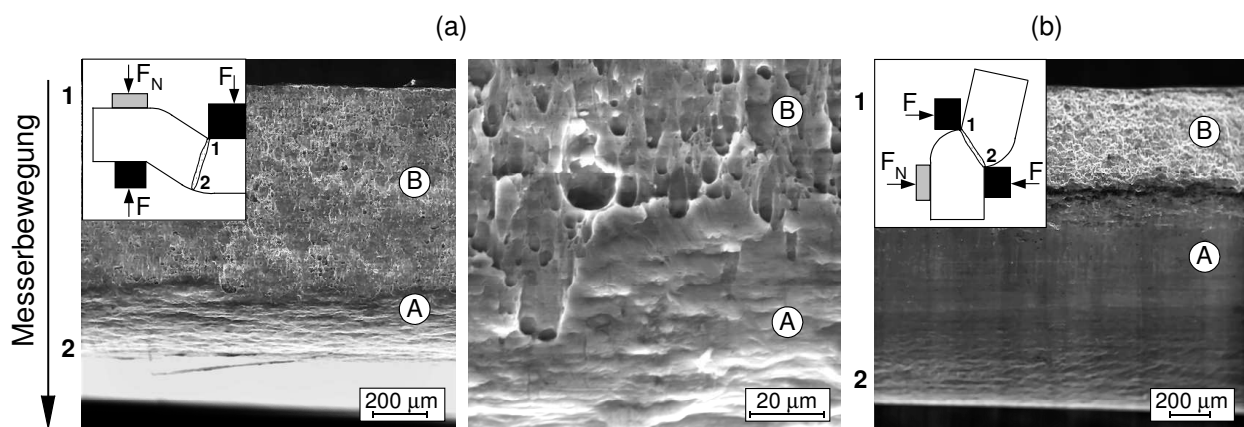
Bruchflächen zerkleinerter Probekörper aus Aluminium AlMg3 (Wanddicke 1 mm) durch eine Reißbeanspruchung mit der Scher- und Reißvorrichtung (a) und dem Schlagwerk (b)
